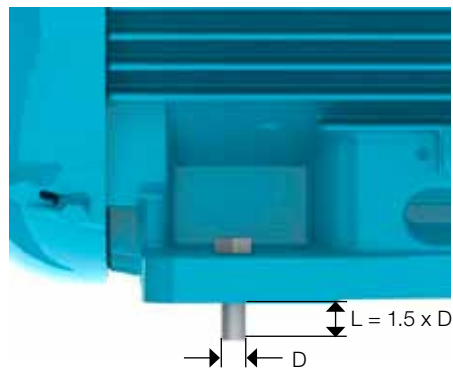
Darstellung der Befestigung des Motors mit FüÙen
